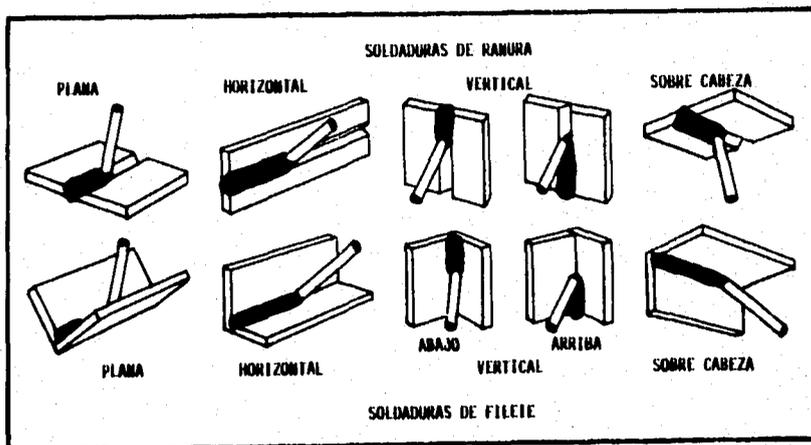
POSICIONES USUALES PARA SOLDADURA.
